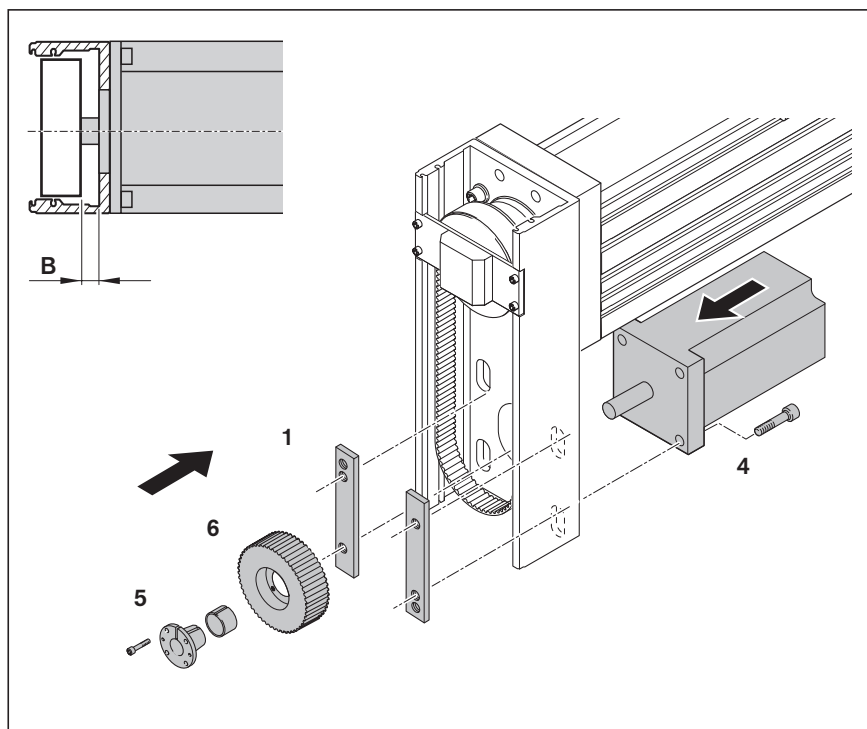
Montagem Montar o motor e a segunda polia ($i = 1$)
